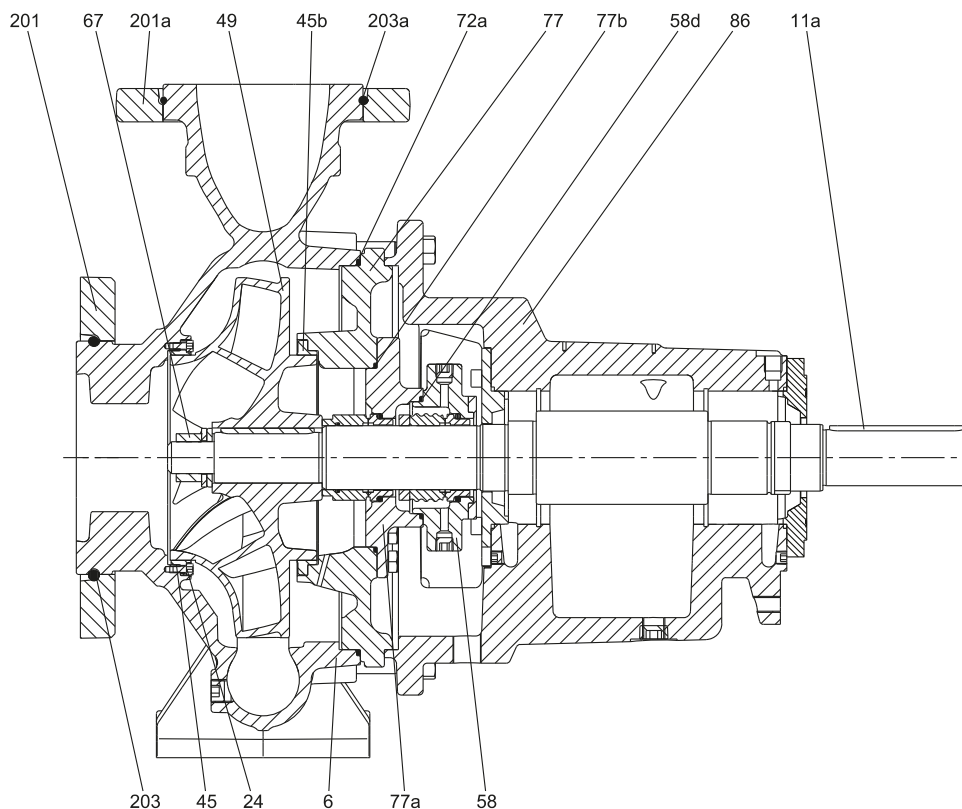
Подшипниковый узел NKG с консистентной смазкой
